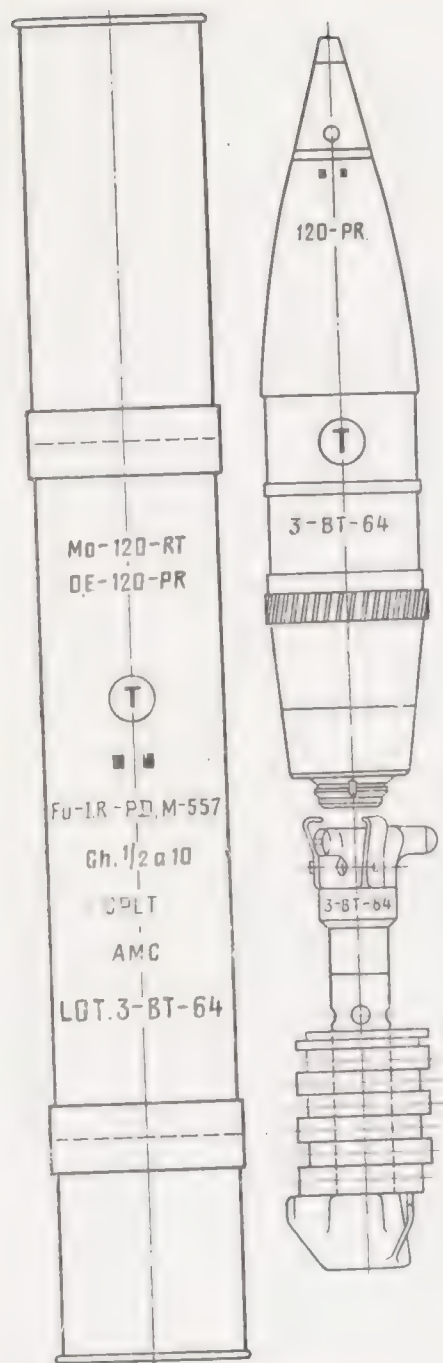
Образец маркировки ОФ снаряда PR.14 и укупорки для выстрела
